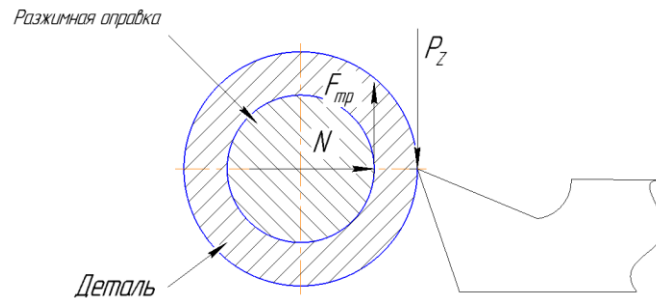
Схема сил, действующих при резании и закреплении заготовки
